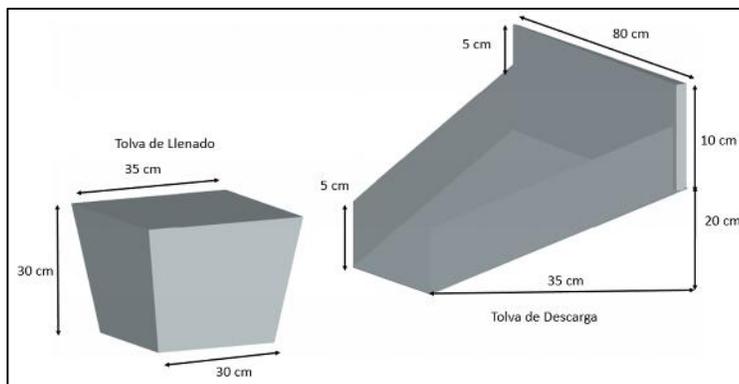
Tolva de llenado y de descarga de lámina galvanizada calibre 26.
